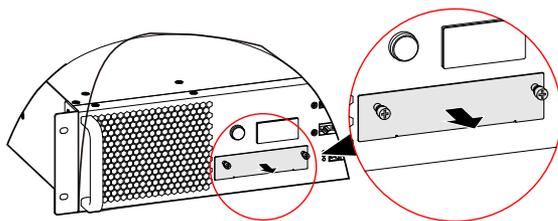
Desmontaje de la cubierta de la tarjeta de expansión
